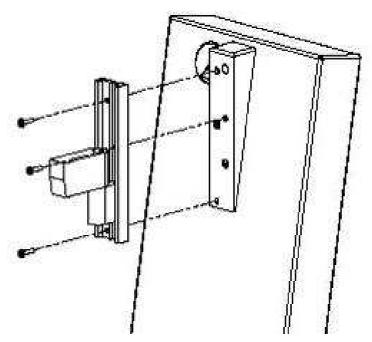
Detailansicht Standfuss; Wandhalter befestigen
